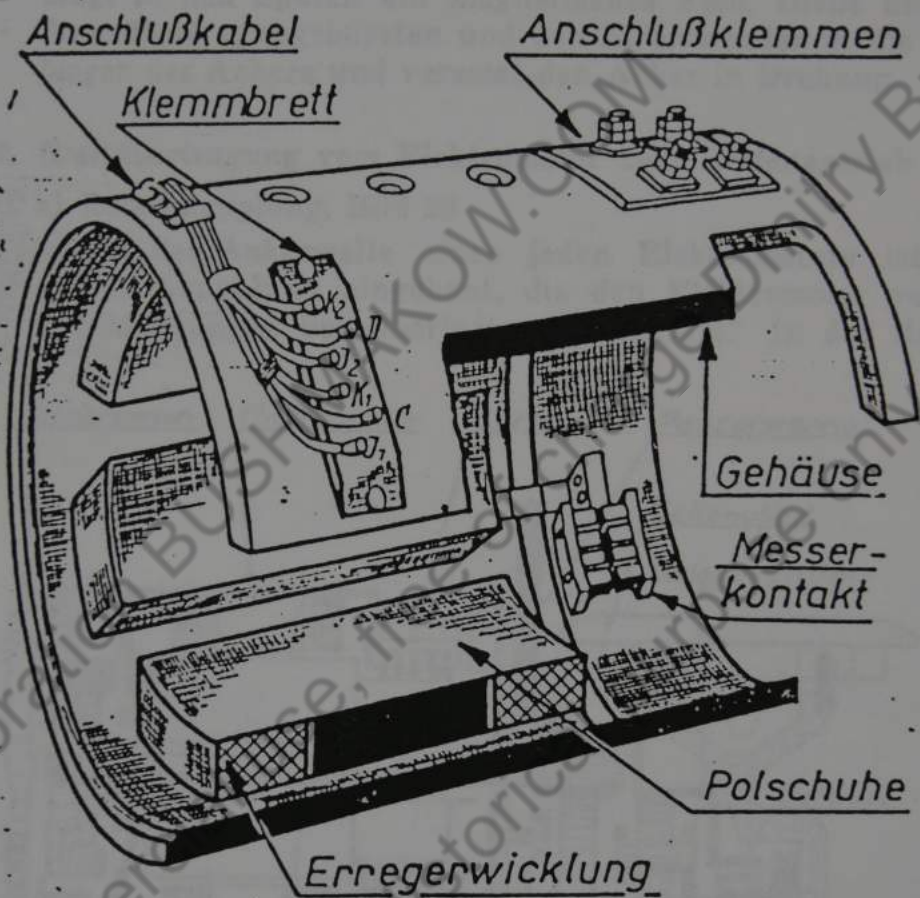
Stromerzeuger- und Elektromotor-Gehäuse
